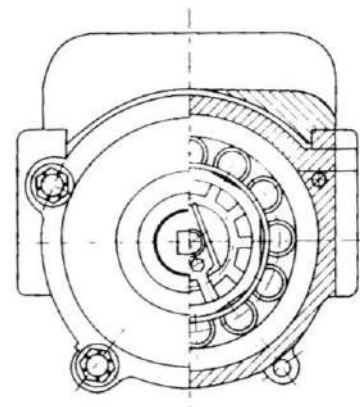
Буксовий вузол з корпусом у вигляді полого циліндру
